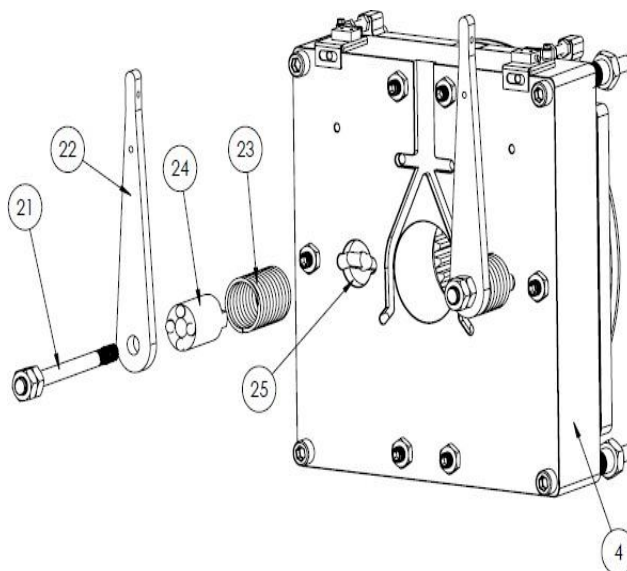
Vista en despiece del freno AEMF1-2-7-8
